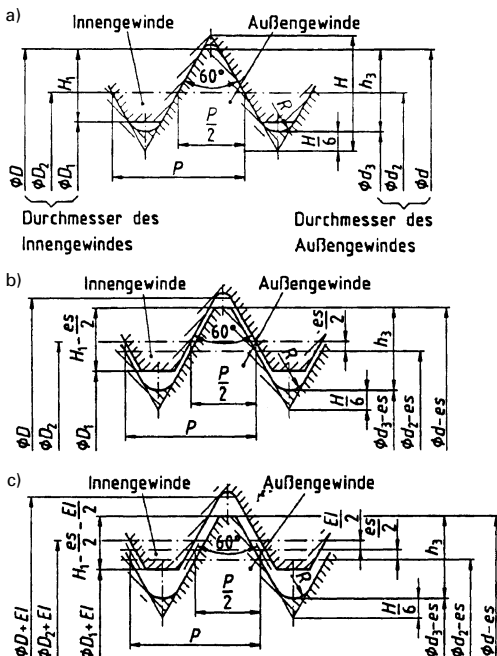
Metrisches ISO-Gewinde, Gewindeprofile nach DIN 13-19
